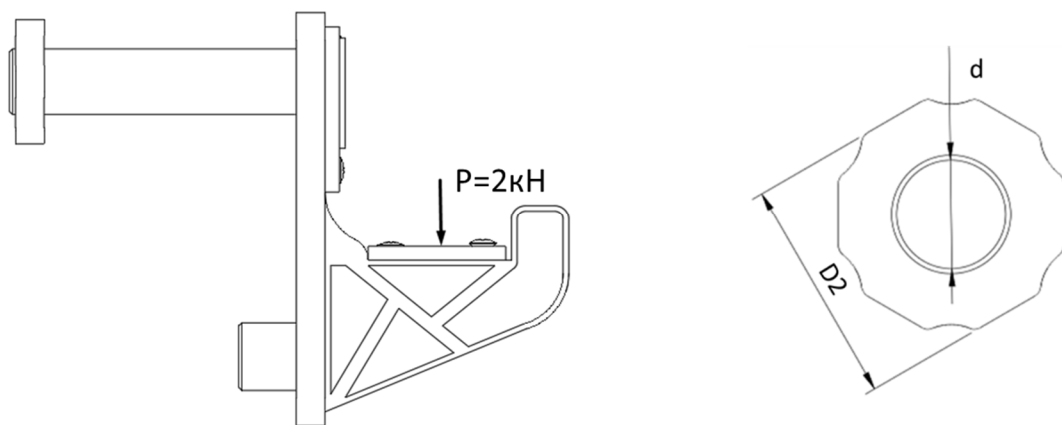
Креслення елементів з'єднувальних конструкцій:
